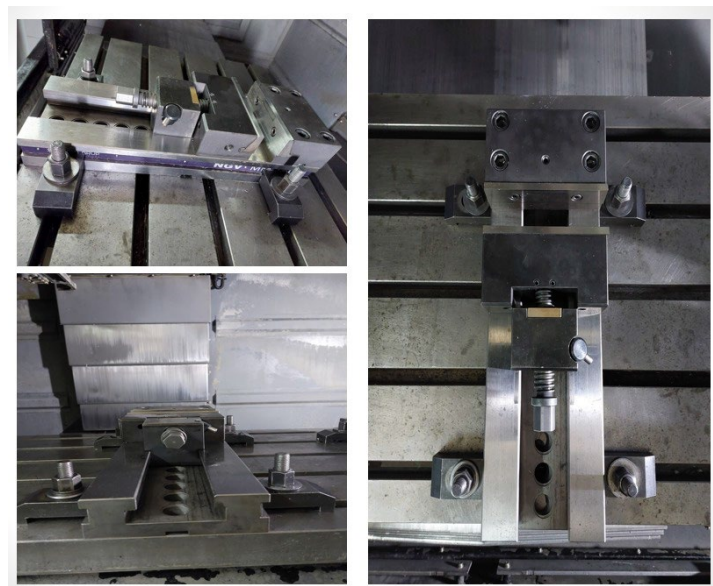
Menghină pneumatică automatizată integrată pe masă de prelucrare CNC
